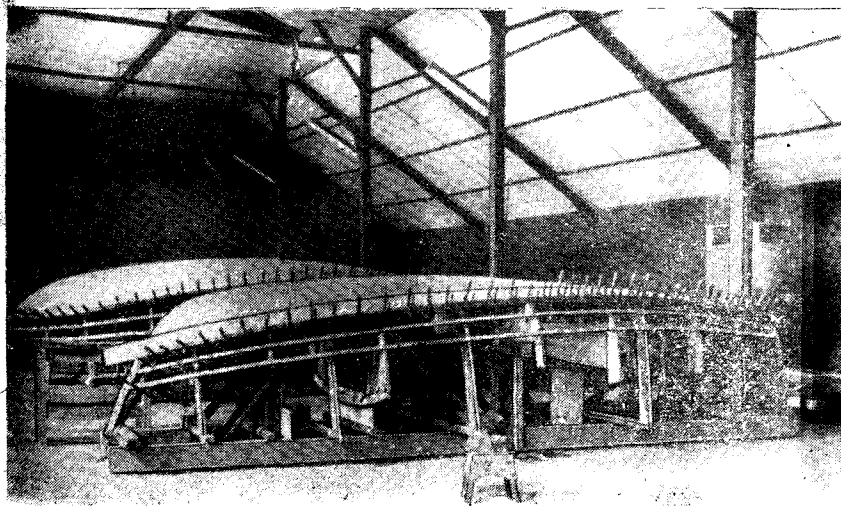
Установка на корпус предварительно отфрезерованного пояса обшивки из фанеры.
